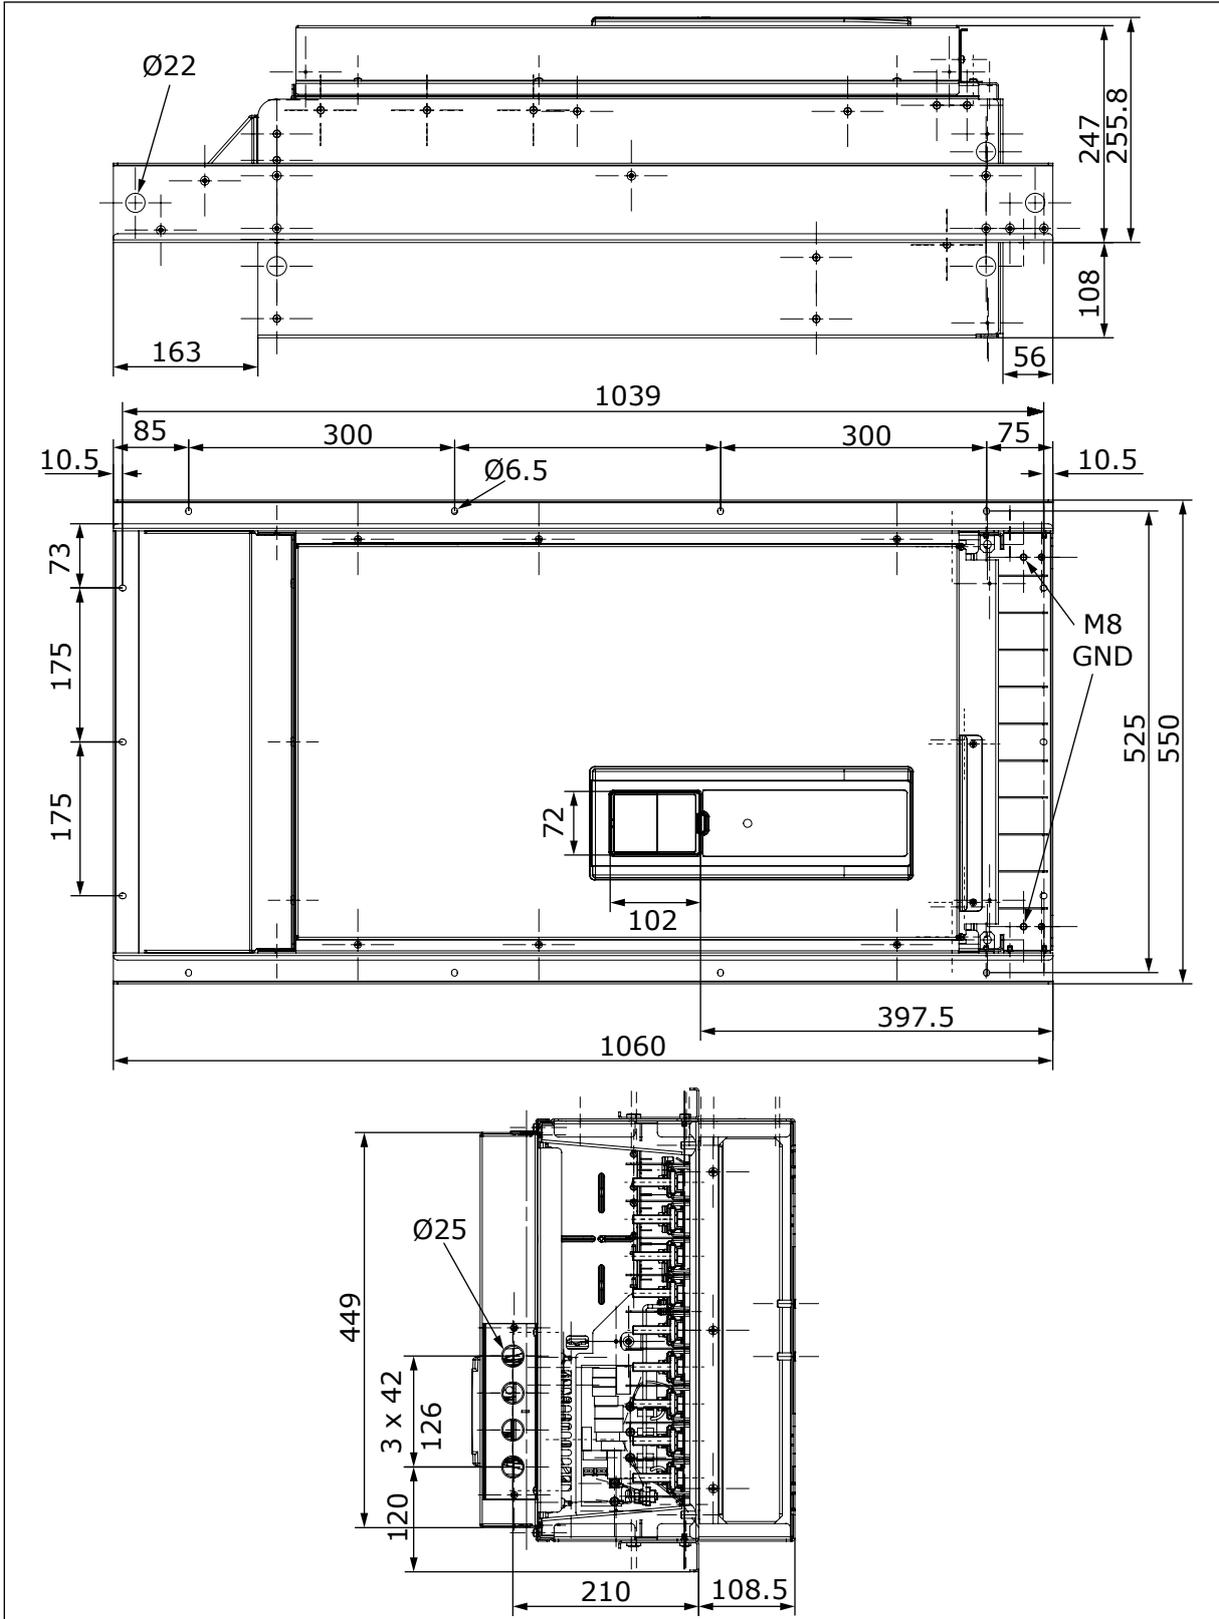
Abmessungen des Frequenzumrichters, Flanschbefestigung, MR9 [mm]
